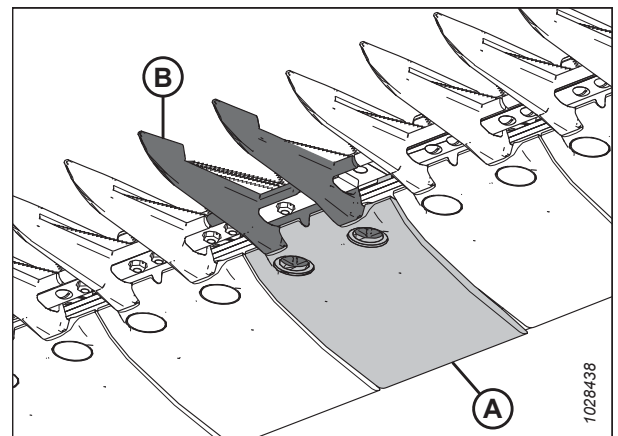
Doigt du couteau central pointu et plaque d'usure
